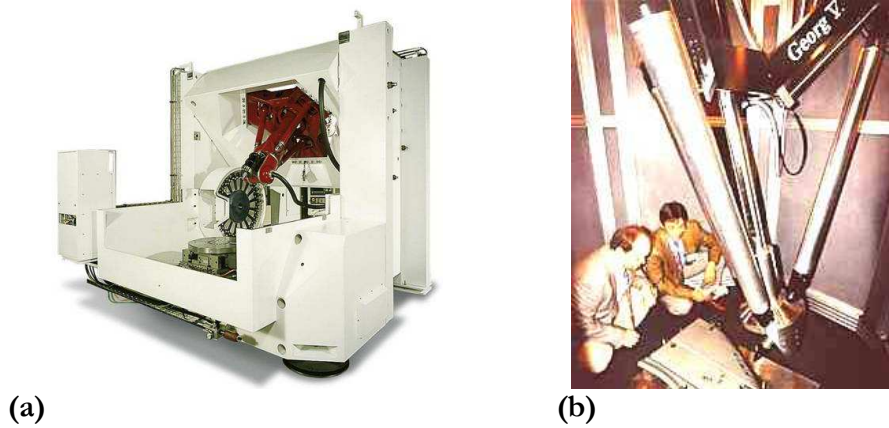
Machines d'usinage à structure hybride à porteur parallèle et poignet sériel : Tripteur de PCI (a) et Georg V (b)
